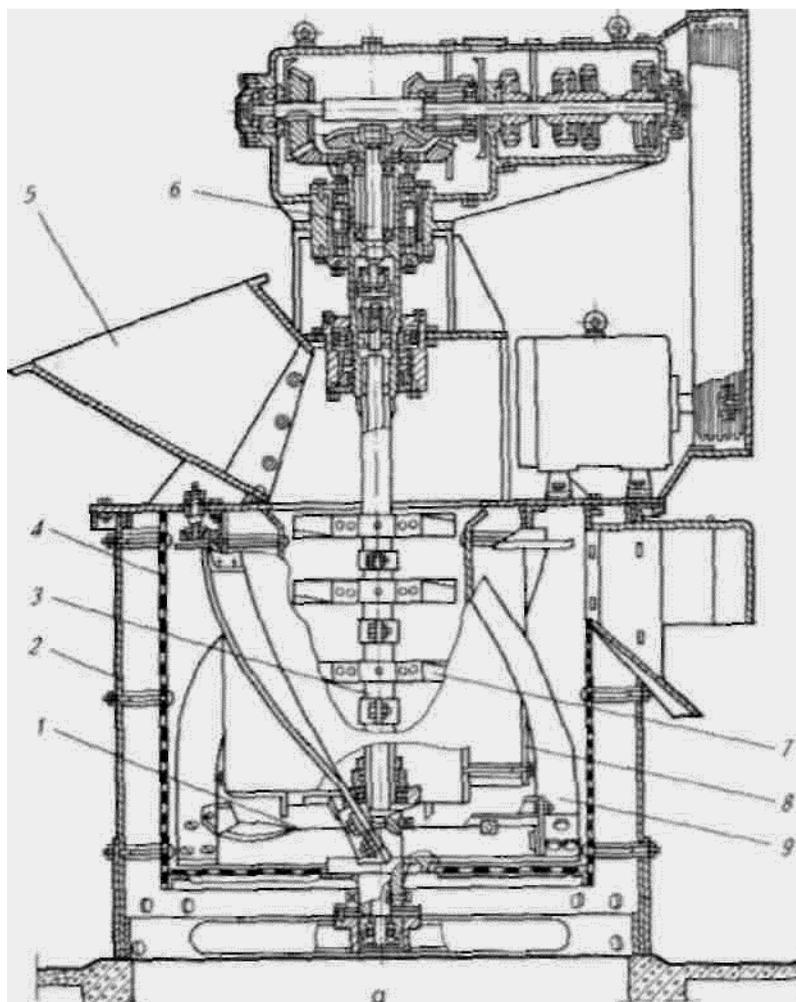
Ударно-центробежная: а - разрез общего вида (1 - крестовина; 2 - корпус; 3 - труба; 4,8- цилиндры; 5- бункер; 6- вал; 7- бич; 9 -лопасть)
